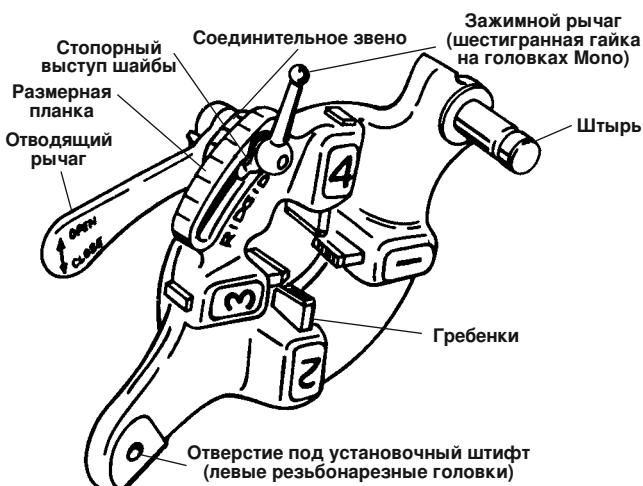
Быстрооткрывающаяся резьбонарезная головка
